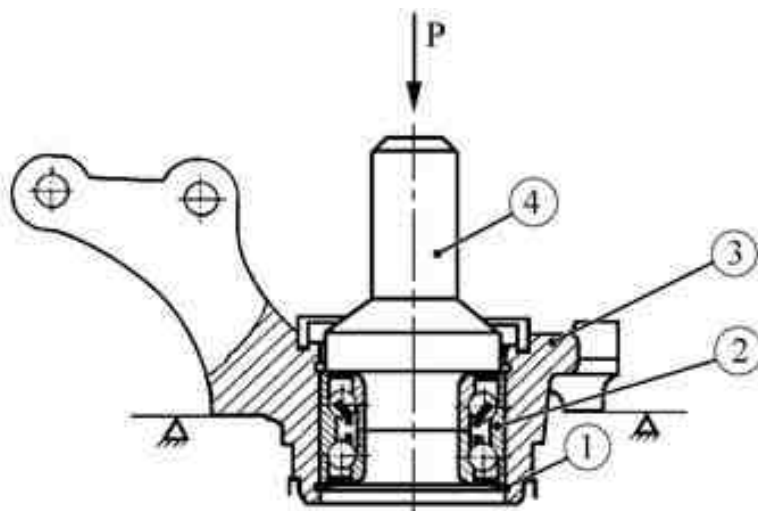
Выпрессовка из кулака и запрессовка в кулак подшипника ступицы переднего колеса:
